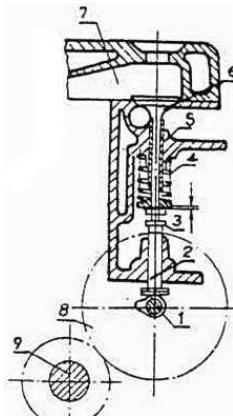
Mekanizmi i shpërndarjes së gazrave me valvula anësore
